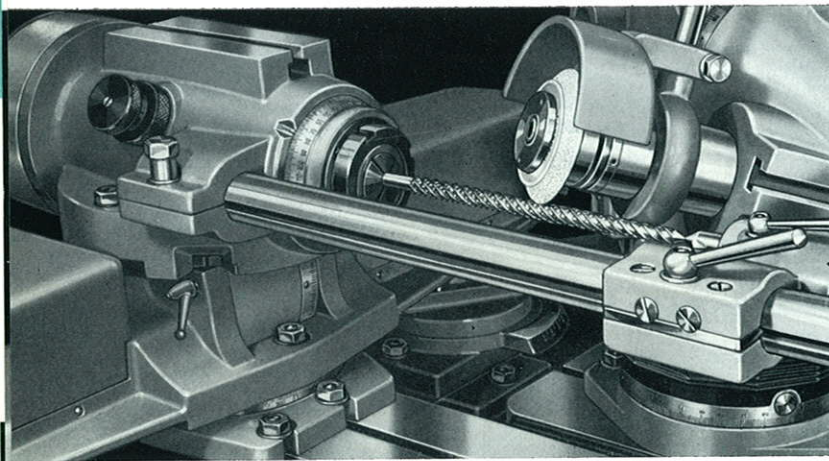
Schleifen der Spanfläche eines spiralverzahnten Gewindebohrers
